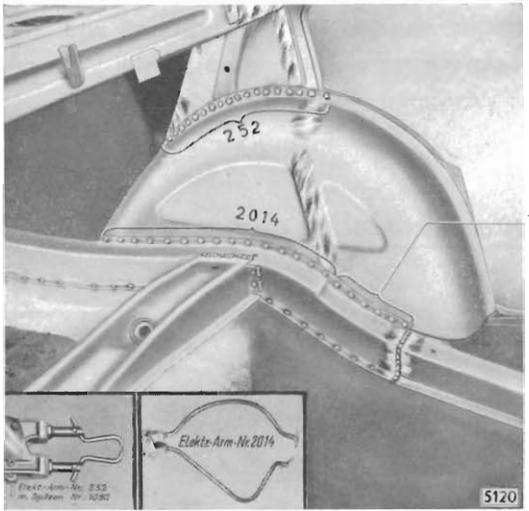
Radeinbau an Seitenwandverkleidung und an Hinterlängsträger zangen- und lichtbogenpunktgeschweißt
